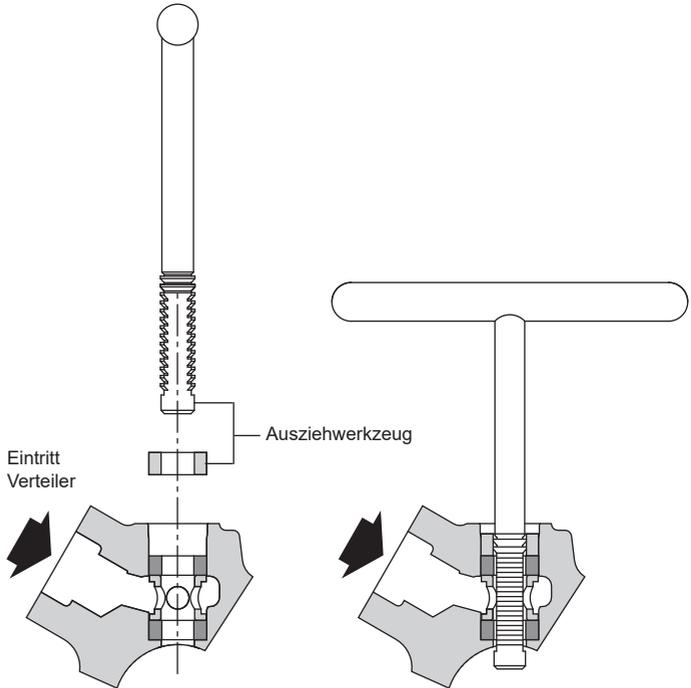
Ausziehwerkzeug für Ventil-Innenteile
